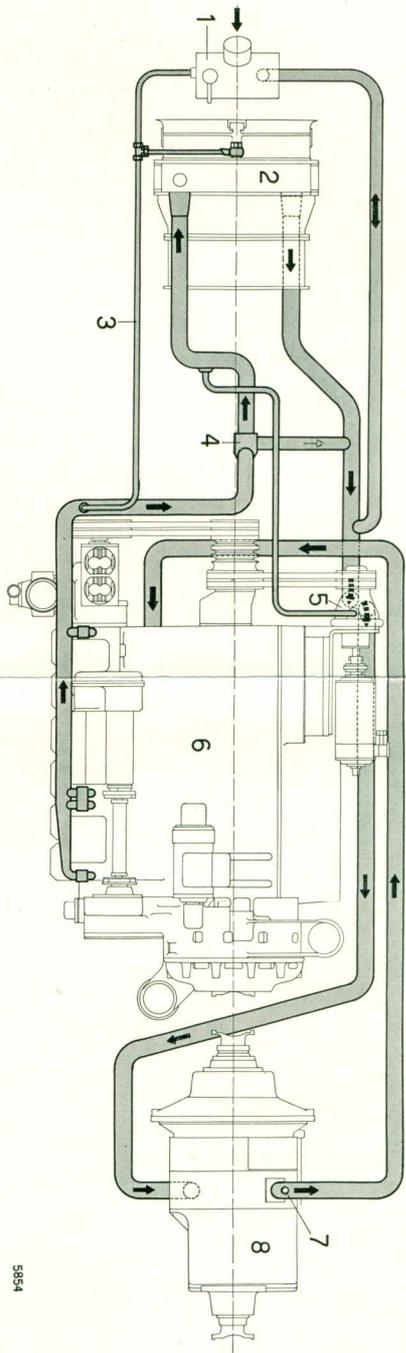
Kühlwasserkreislauf im Kühler-Getriebe-Motor
